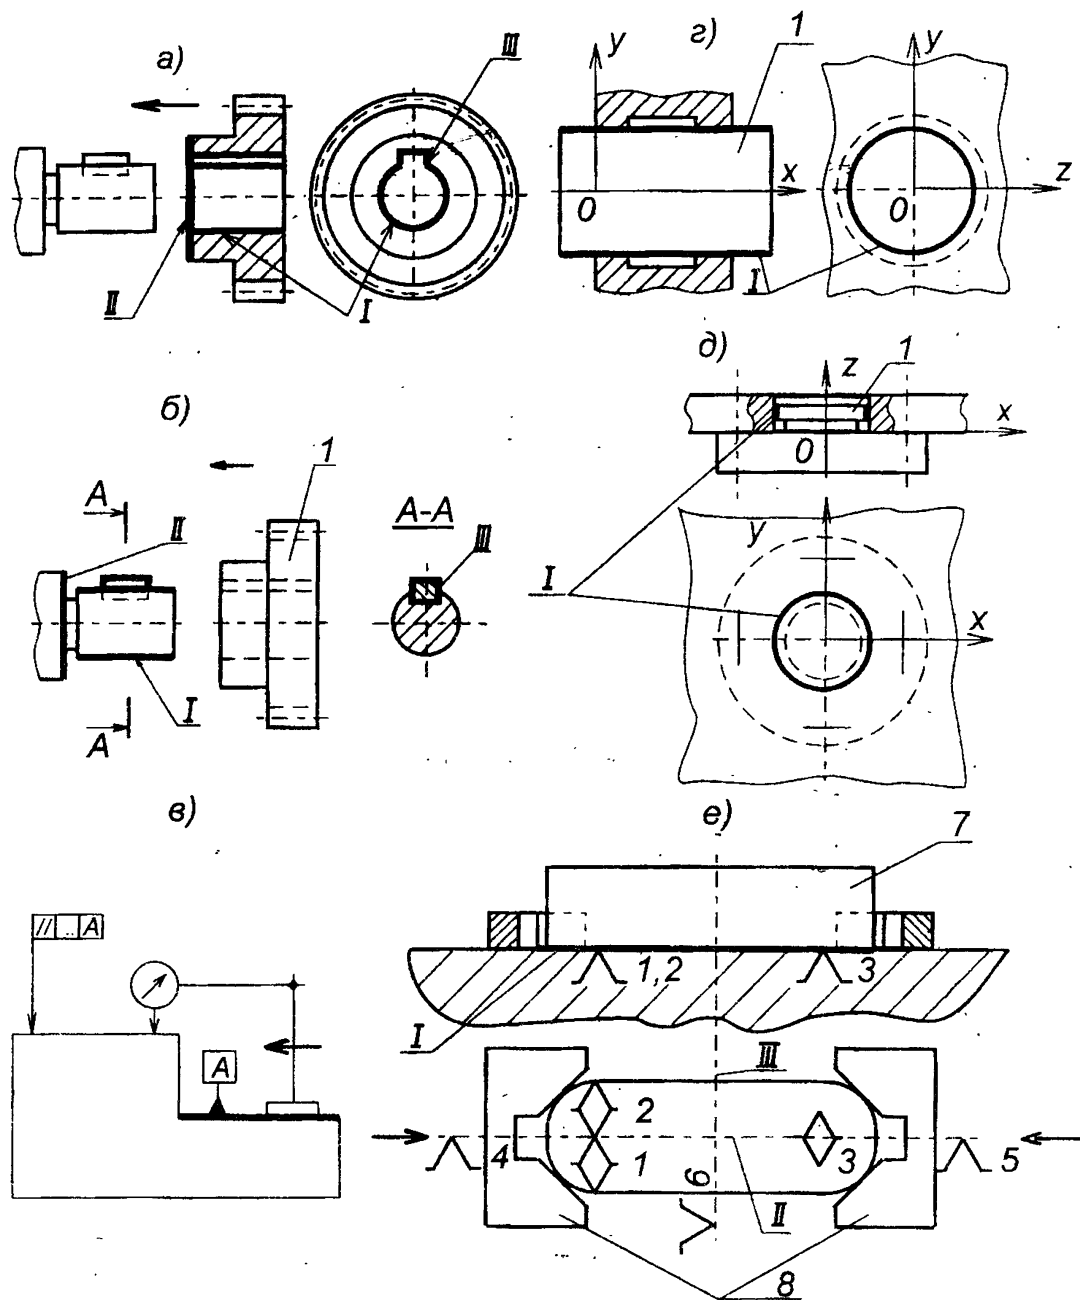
Примеры установок : а-комплект основных баз шестерни -I, II, III; б - комплект вспомогательных баз вала со шпонкой - I, II, III; 1 - присоединяемая деталь; в - измерительная база детали - A; г - двойная направляющая база детали - I; д - двойная опорная база детали - I; 1 - деталь; е - установочная явная база заготовки - I; направляющая скрытая база заготовки - II; опорная скрытая база заготовки - III; L..6 - опорные точки; 7 - заготовка; 8 - губки самоустанавливающихся тисков
